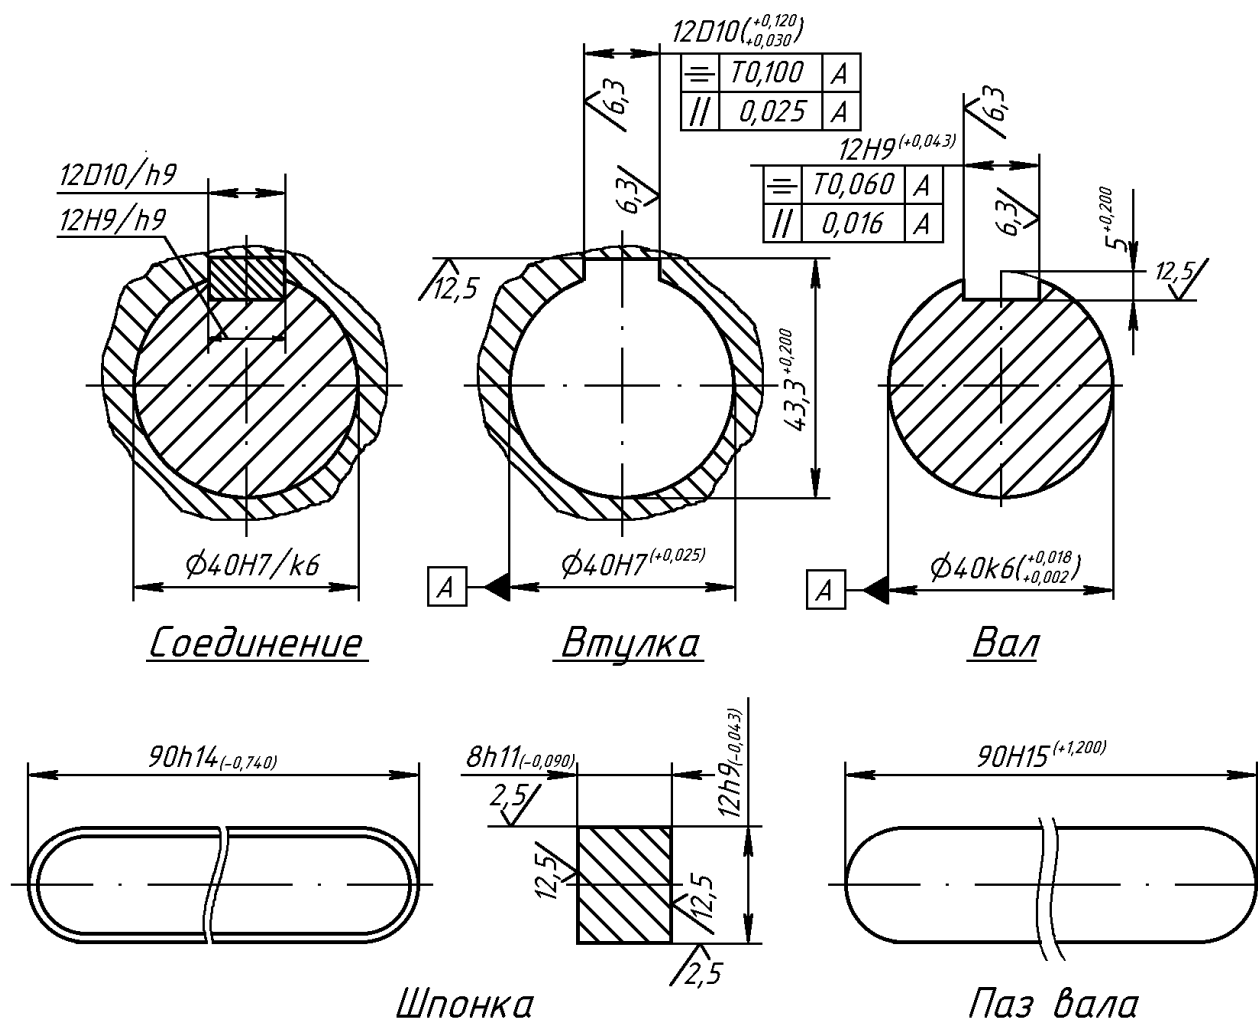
Чертежи шпоночного соединения и его деталей
